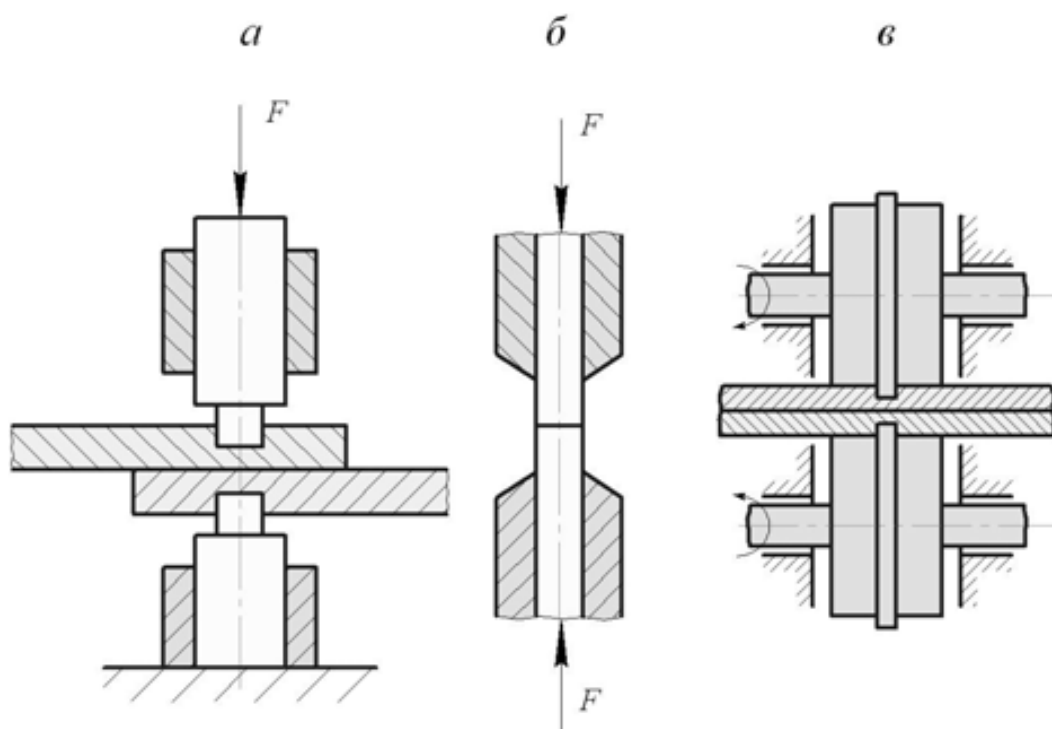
Схема холодной сварки: *а* – сварка внахлестку (точечная); *б* – сварка встык; *в* – шовная сварка
